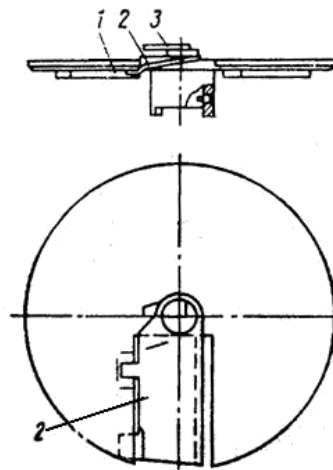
Верхній диск із ножем: 1-диск; 2-змінний ніж; 3- спеціальний болт для закріплення ножа.
